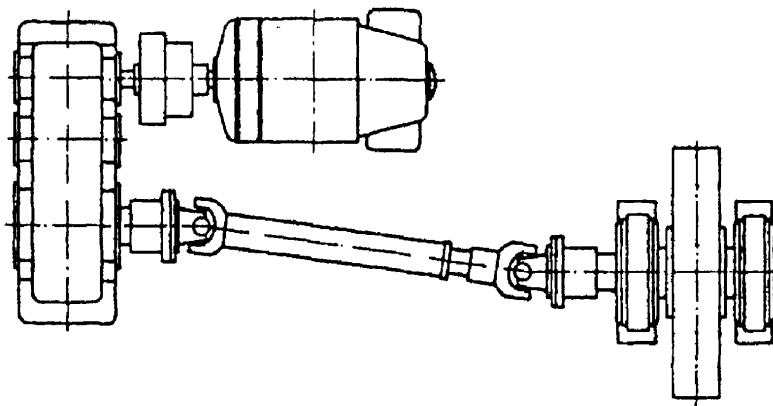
Установка шарнирного вала для привода одного колеса
